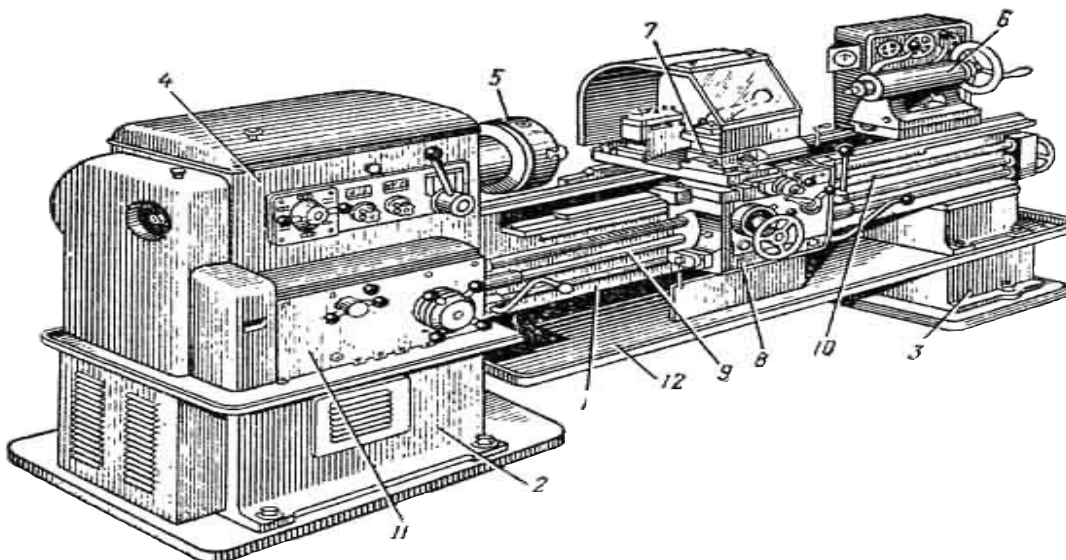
Універсальний токарно-гвинторізний верстат 1K62
